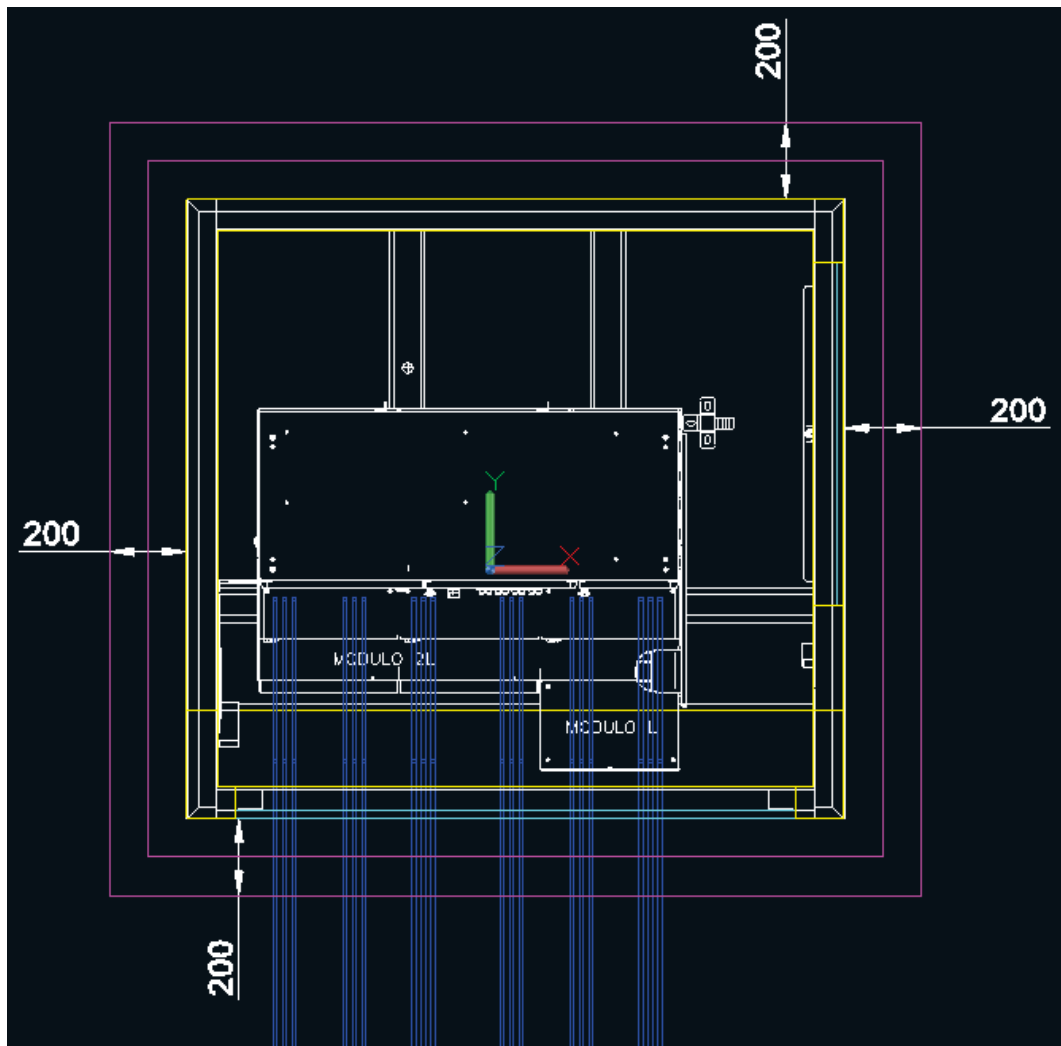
Vista en planta de la instalación (3L [Semi]) (cotas en mm).
